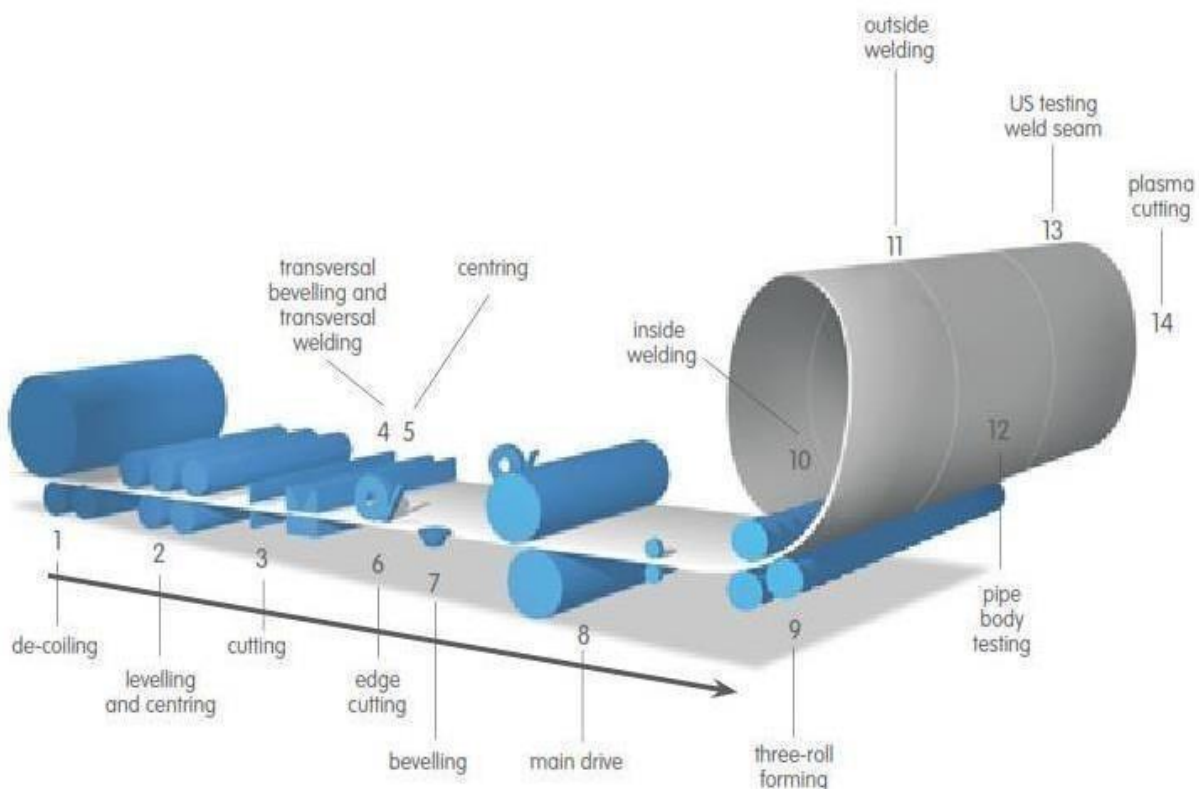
Technique de fabrication des pipes soudés en spirale
